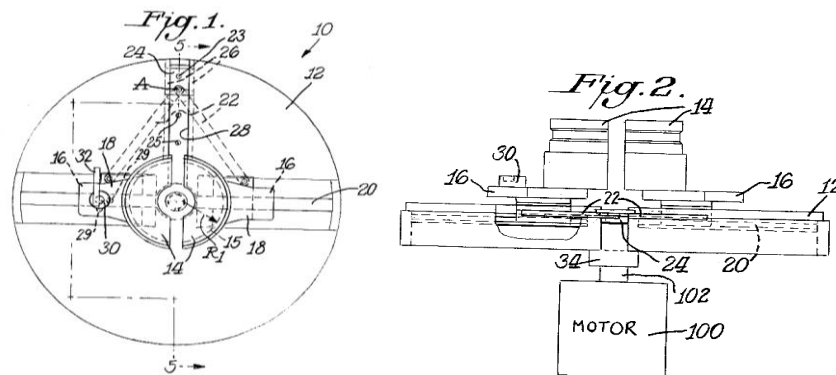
Vista en planta superior Fig. 1 y vista en alzado frontal Fig. 2.
